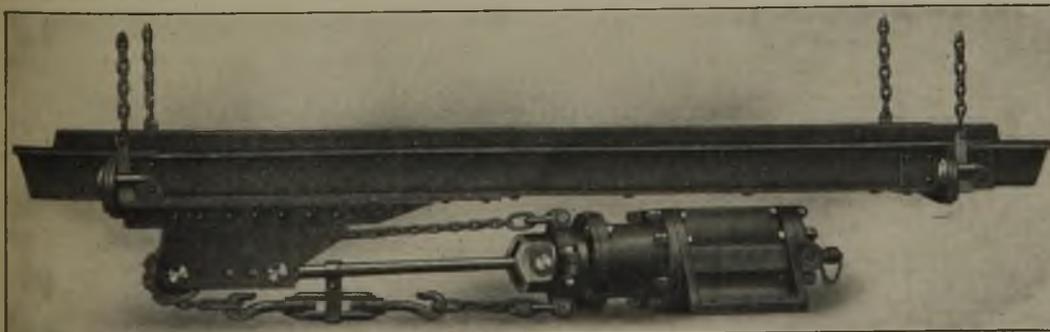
Zweiseitig wirkender Kugelsteuerungsmotor mit Spannvorrichtung.
